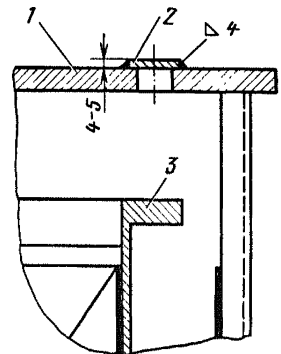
Заделка отверстий в листе крышки кожуха.
